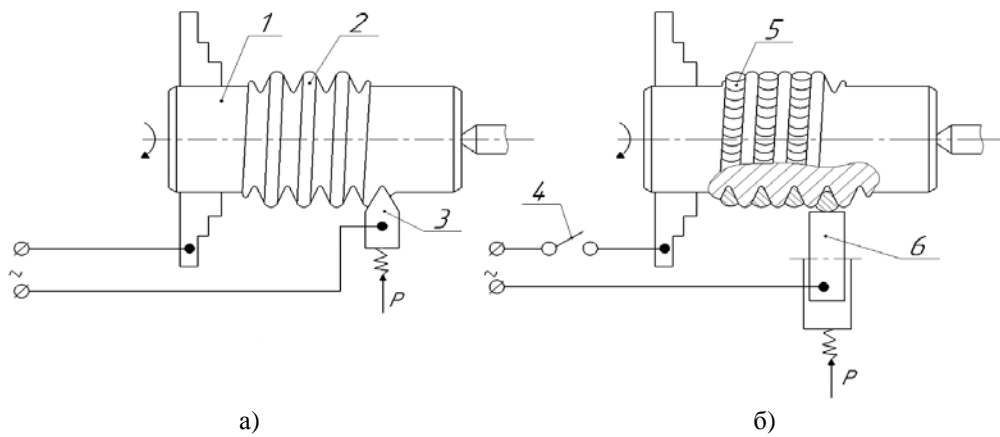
Схема наплавки в высаженную канавку: а - схема электромеханической высадки; б - схема электроконтактной наплавки; 1 - деталь; 2 - высаженная канавка; 3 - высаживающая пластина; 4 - прерыватель тока; 5 - наплавленный валик присадочного металла; 6 - наплавляющий ролик
